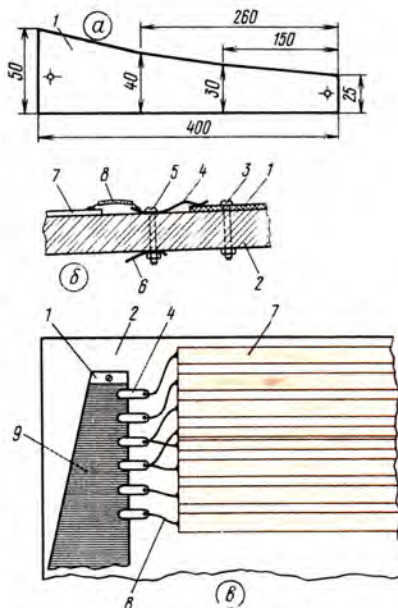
Конструкция самодельного резистора и расположение его на доске: а — каркас резистора; б — крепление резистора и пружинящих пластинок; в — расположение резистора, пружинящих пластинок и шин рабочего поля на классной доске; 1 — резистор; 2 — доска; 3, 5 — болты; 4 — пружинящая пластинка; 6 — контактный лепесток; 7 — шина рабочего поля; 8 — проводочная перемычка; 9 — обмотка резистора
